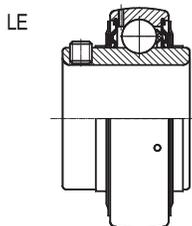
Регулируемые шариковые подшипники с винтами - тип LE
